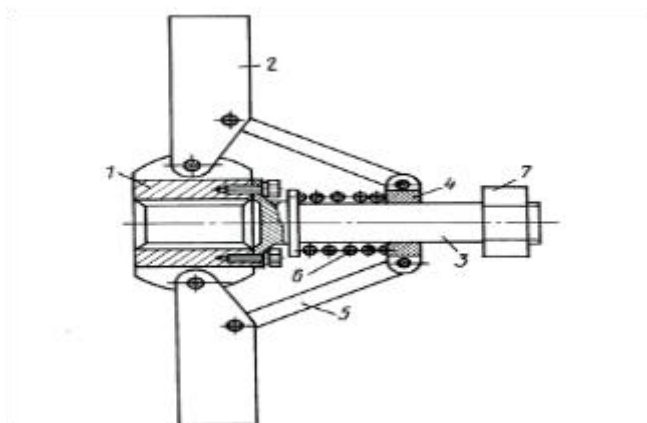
Общий вид фрезерного рабочего органа
